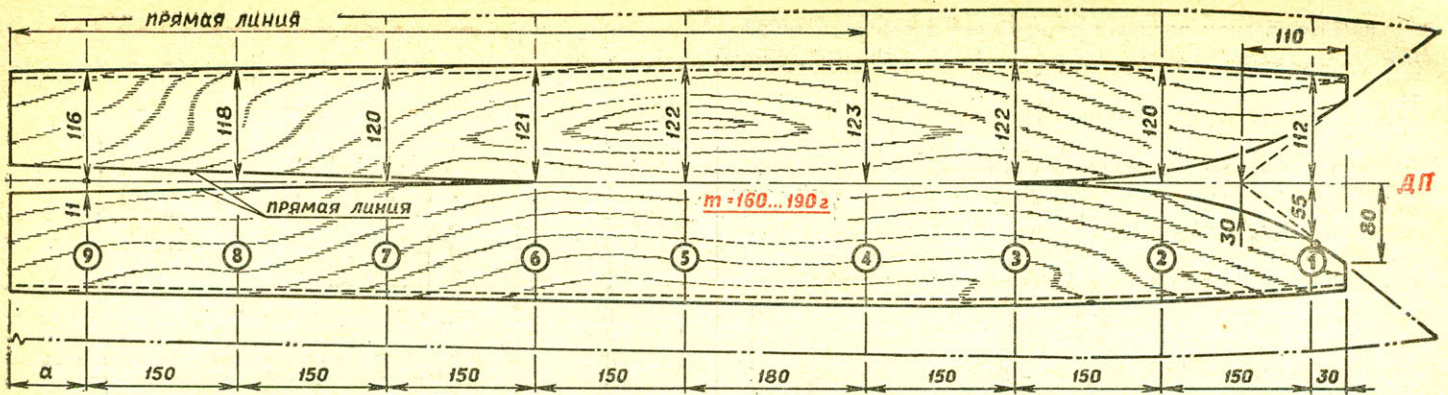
Основные размеры раскроя листа фанеры для изготовления корпуса (размер «а» определить после сборки корпуса, линией условного контура показаны размеры ранее применявшейся выкройки).
